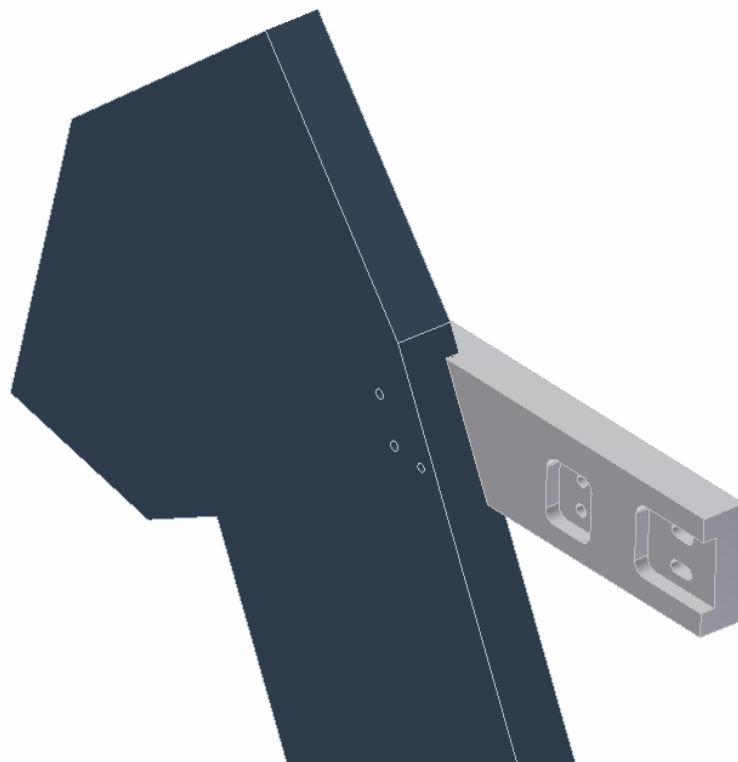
Schematický náčrtek redukce mezi držákem tubusu a motorku a spojovacím ramenem. Uvedené hodnoty jsou v mm.
